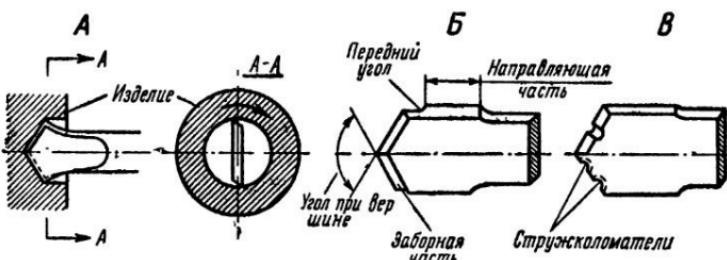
Первое сверло: *А* — сверление первым сверлом; *Б* — сверло с направляющей частью; *В* — сверло со стружколомающими канавками.
